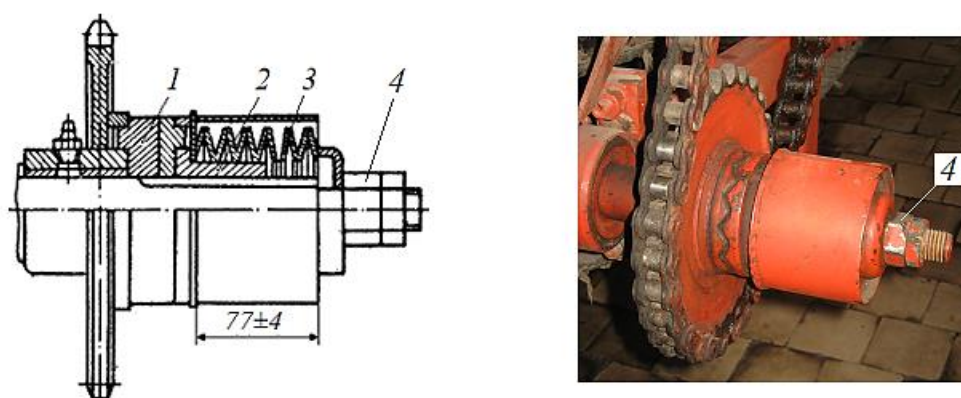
Регулювання запобіжної муфти: 1 - зубчата шайба; 2 - шлицева втулка; 3 - тарілчаста пружина; 4 - гайка
